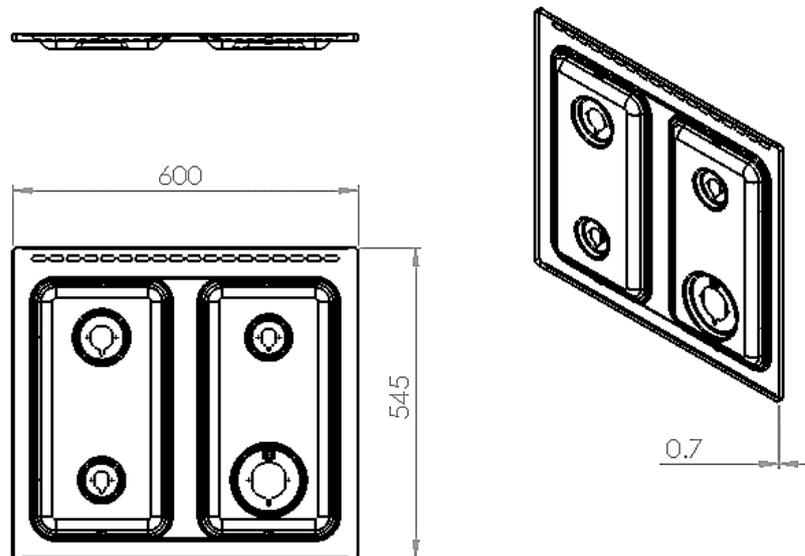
Forme de la pièce à réaliser et ses dimensions.
